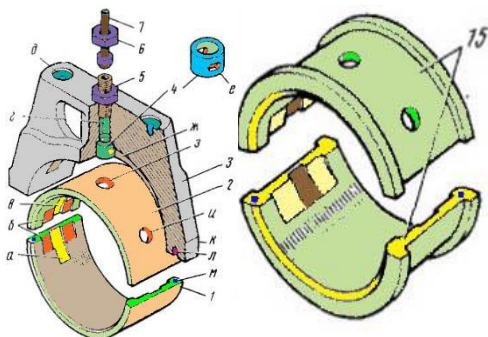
Коренные подшипники коленчатого вала дизеля 310DR
